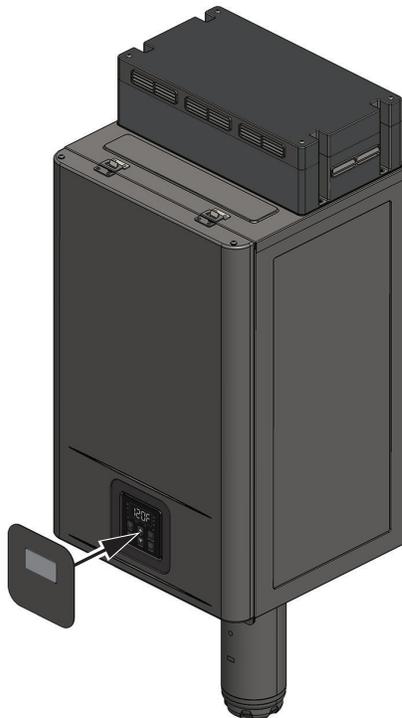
Installation de la plaque de recouvrement du tableau de commande
